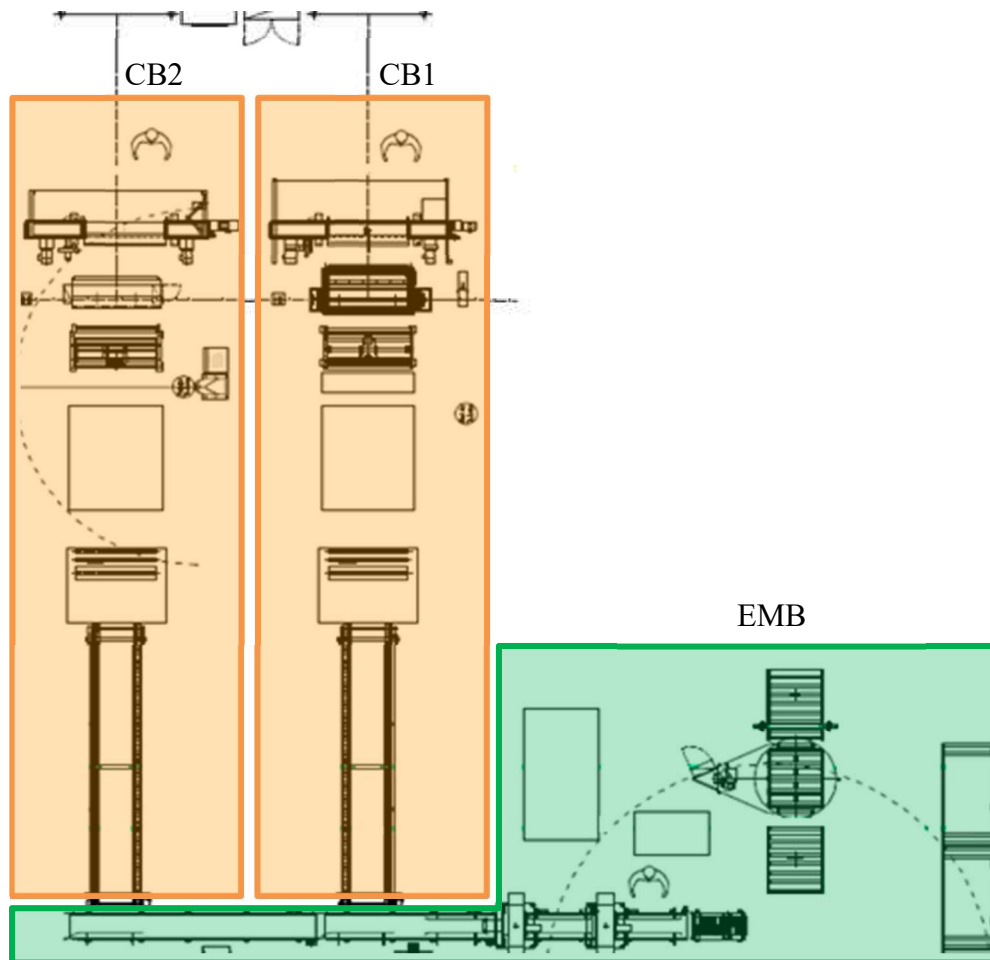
Layout CBE e delimitação de CB1, CB2 e EMB
